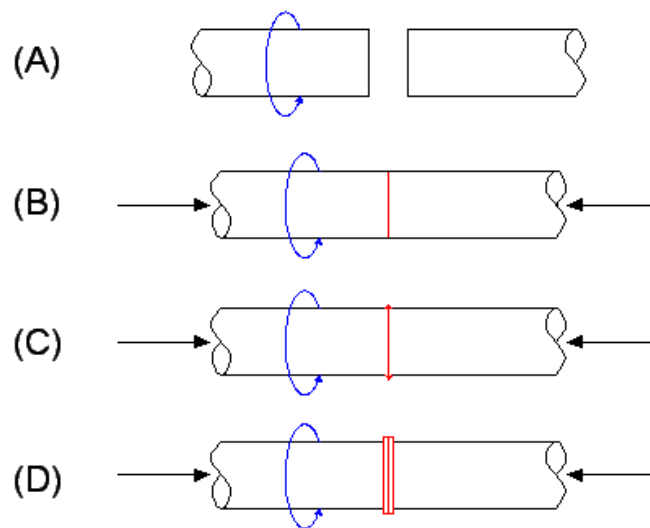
Soldadura por fricción, [11, p. 2]
